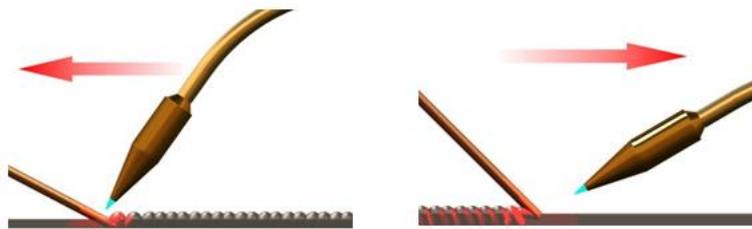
técnicas de soldeo (a izquierdas, en el lado izquierdo y a derechas, en el lado derecho)
